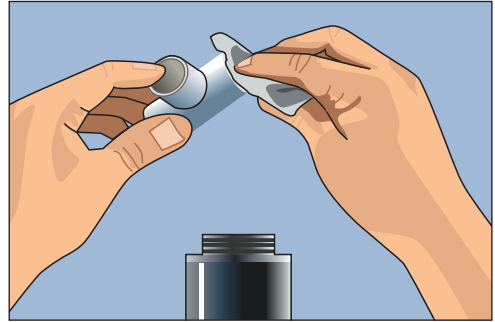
Обрабатываем места склеивания фитинга и трубы очистителем
